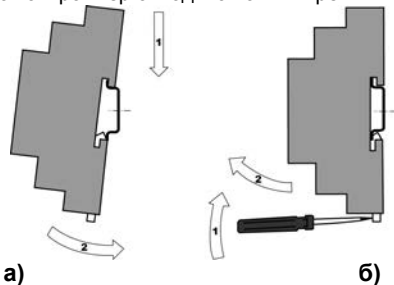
Монтаж контроллера с креплением на DIN-рейку
